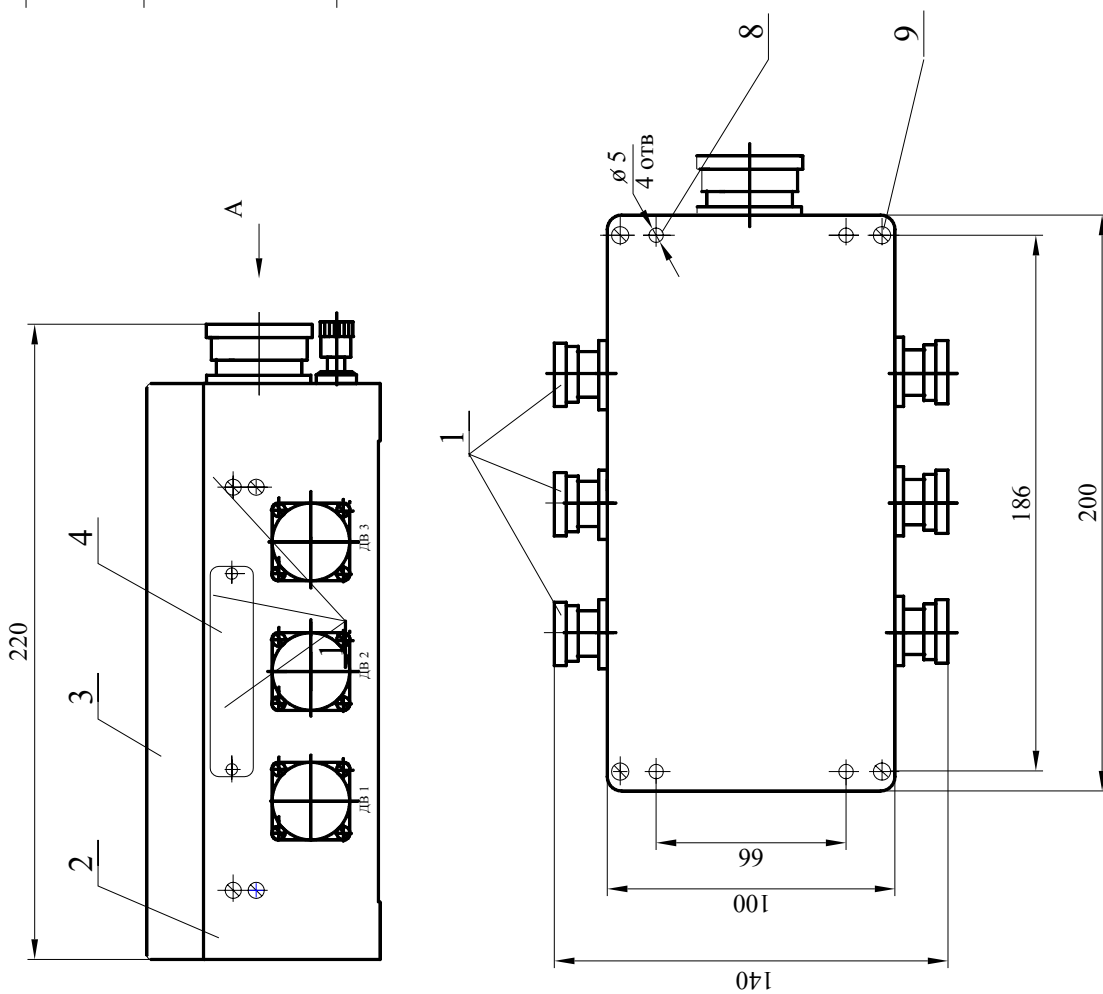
Габаритно - установочные размеры блока согласующего БС-16-11-1
